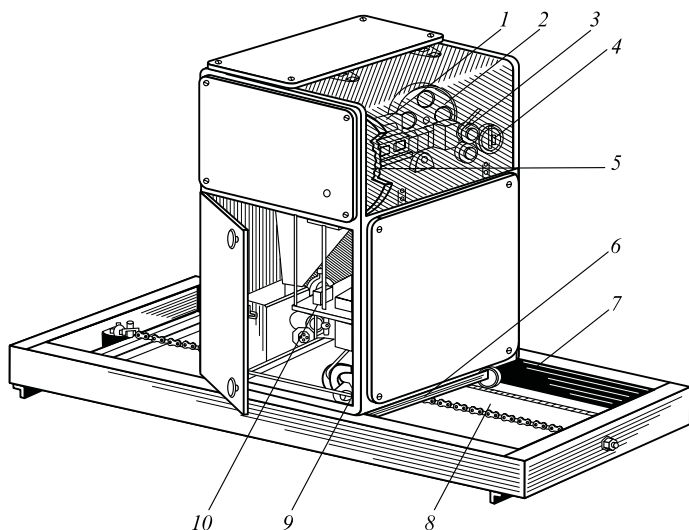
Механизм для отмеривания, резки и укладки кабеля на инвентарный барабан:
